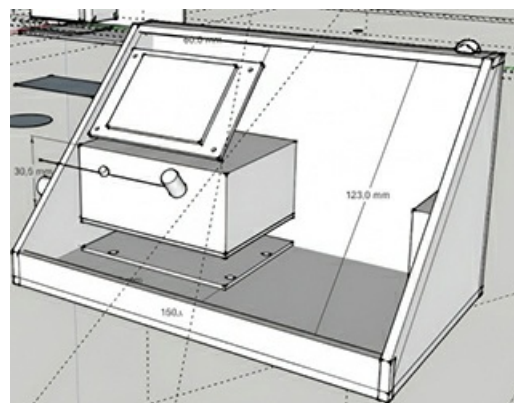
Внешний вид корпуса устройства, нарисованный в программе SketchUp
